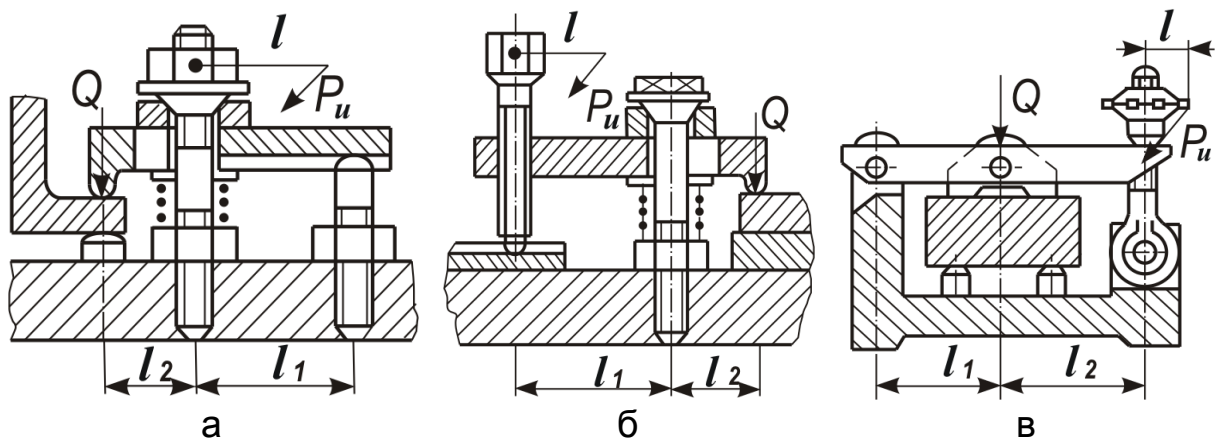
Конструкции прихватов: а, б – с регулируемой опорой; в – с откидной планкой; l_1, l_2 – плечи рычагов
